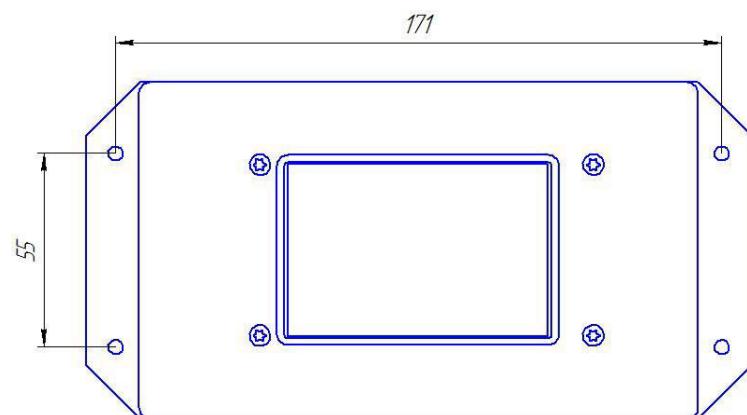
Схема расположения отверстий крепления корпуса TPI-04
